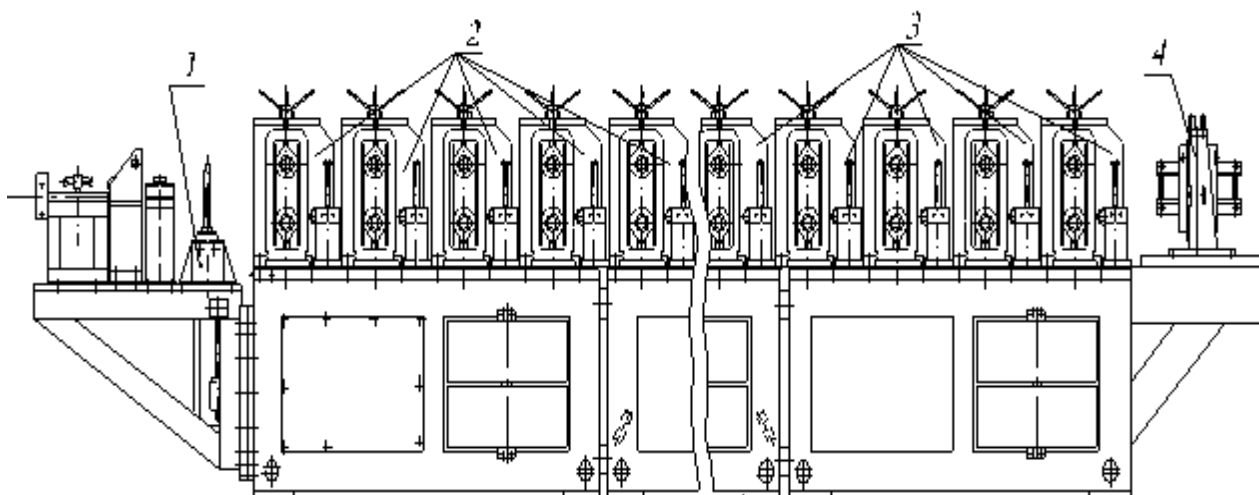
Расположение оснастки на профилегибочном станке:
